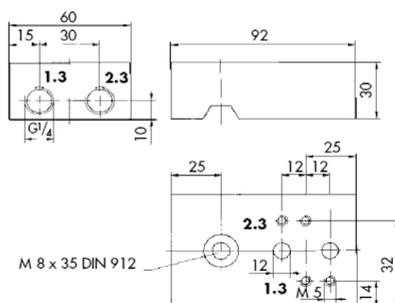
Placa adaptadora puente NAMUR (dimensiones en mm)
